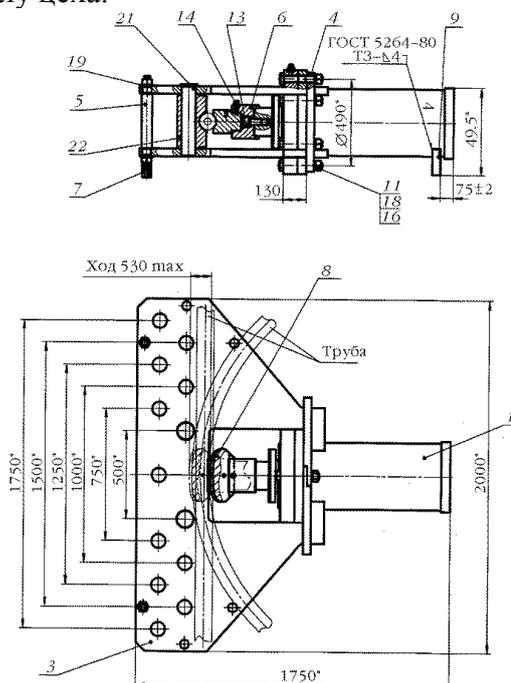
Трубогиб: 1 – гидроцилиндр; 2 – центральный силовой сегмент; 3 – верхняя плита; 4 – упор; 5 – боковой поворотный силовой сегмент; 6 – стяжная шпилька; 7 – гайка; 8 – шпандырь; 9 – стопор; 10 – проточка; 11 – втулка; 12 – стяжное кольцо; 13 – подставка; 14 – стяжные болты
